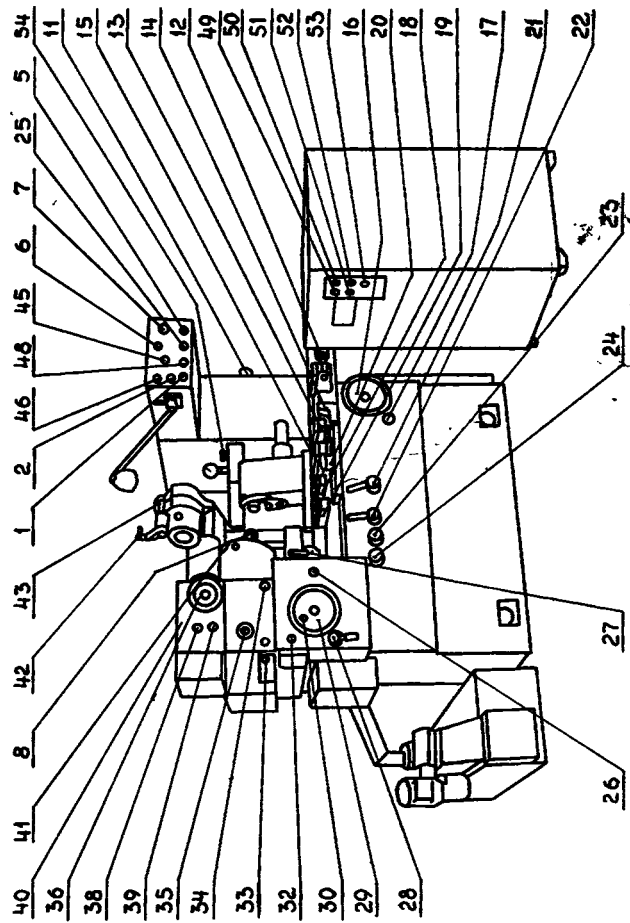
Общий вид станка модели 3К225А с обозначением органов управления и наладки
